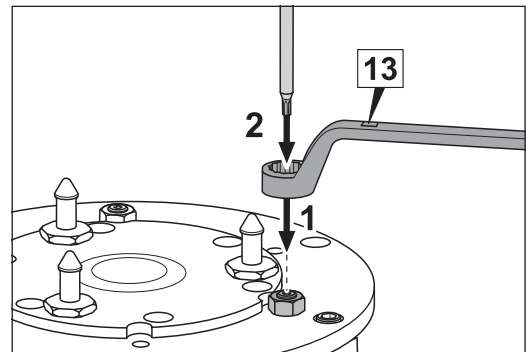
Den Ringschlüssel an der Mutter einer Einstellschraube ansetzen (1) und den TORX-Schraubendreher in den Gewindeschacht der Einstellschraube stecken (2).
